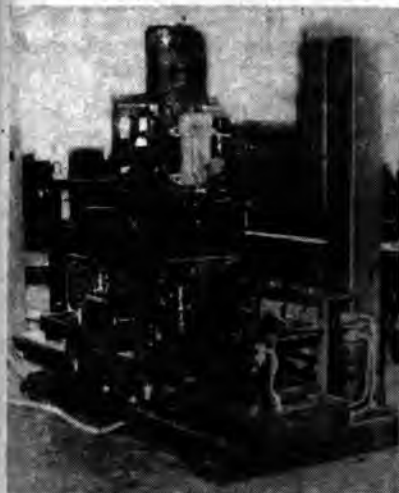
Экспериментальный станок для фрезерования гнукотклеенных заготовок
